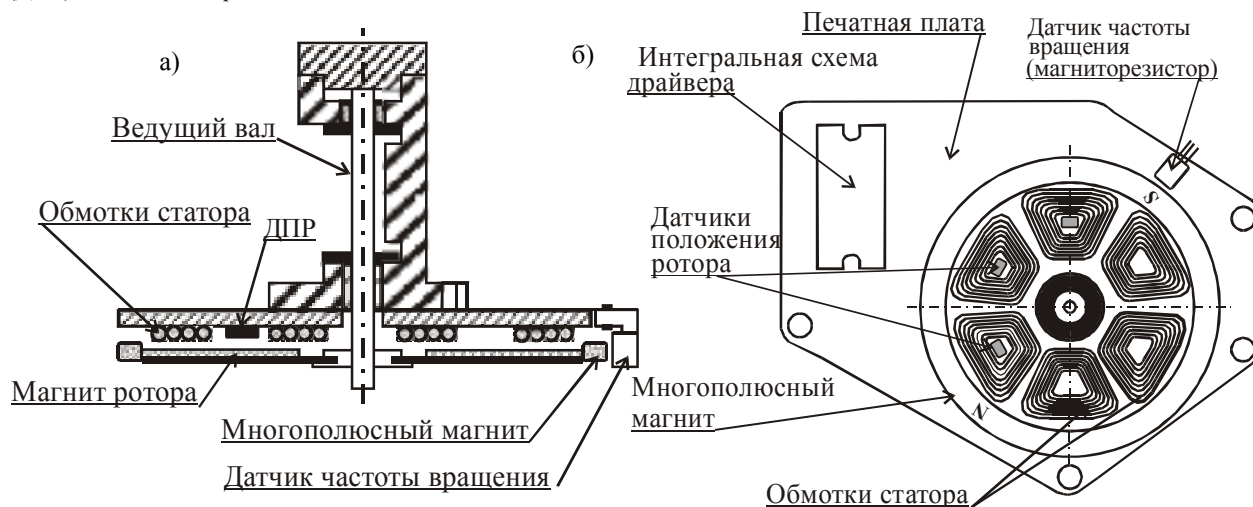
Бесколлекторный электродвигатель ведущего вала видеомагнитофона: а – конструкция; б – статор
